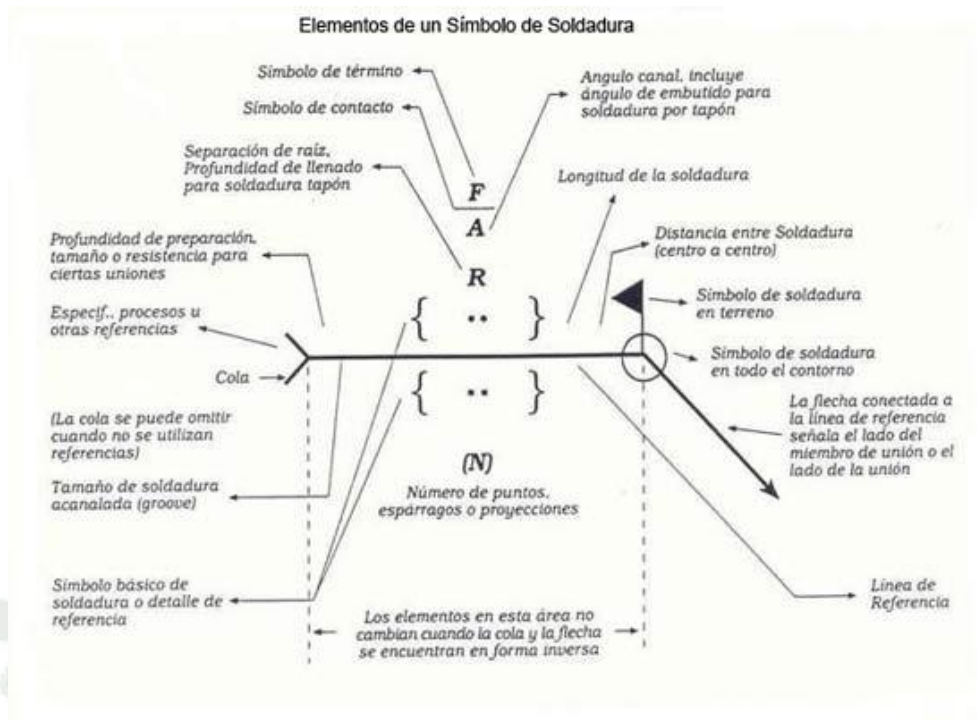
Elementos de un símbolo de soldadura.
